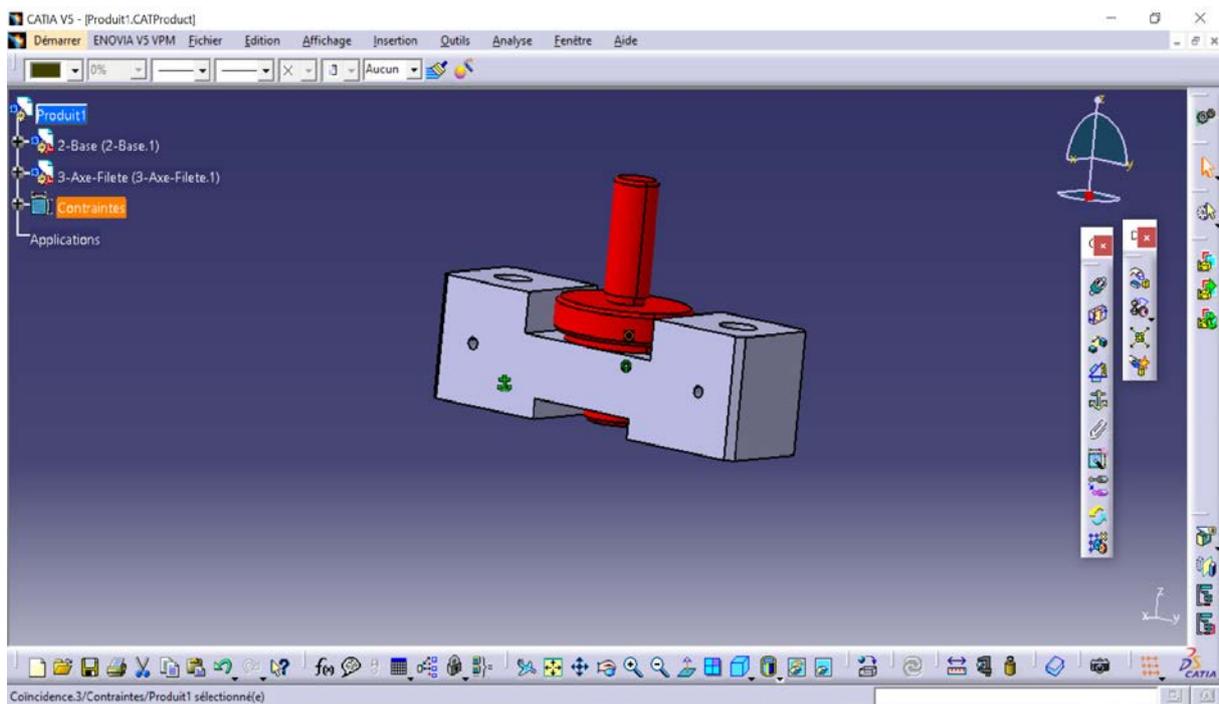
Assembly Design des Pièces 2 et 3 [1], [2]
